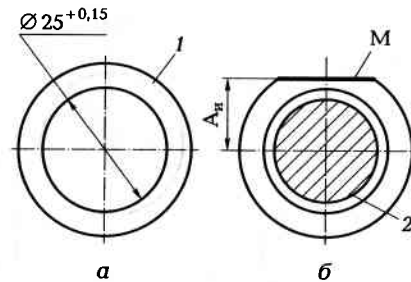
Схема установки (а) заготовки на цилиндрический установочный элемент при фрезеровании (б) плоскости
